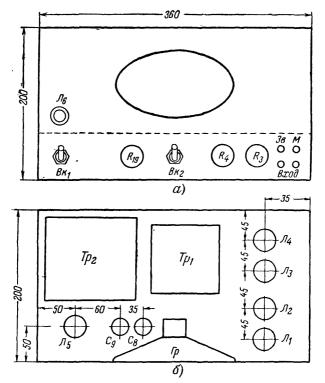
Расположение деталей усилителя для школьного радиоузла.
